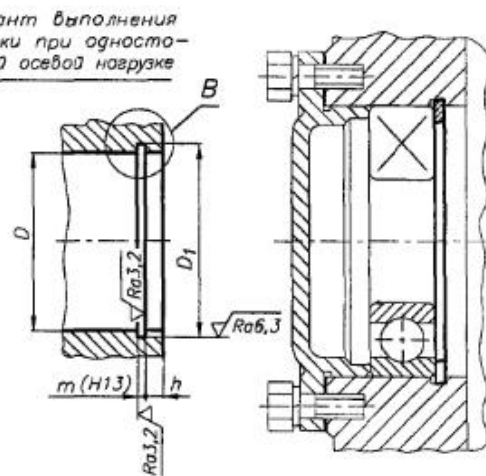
Закрепление наружного кольца подшипника качения в корпусе с использованием пружинного кольца
